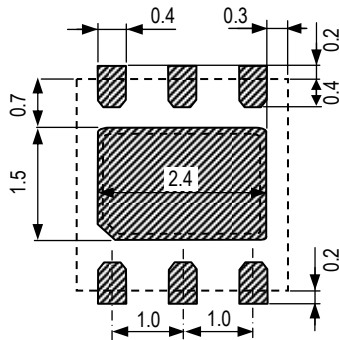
推荐 sht2x 的 PCB 设计尺寸。单位为 mm。裸焊盘（中间焊盘）与 NC 可保持悬浮或接地。外围虚线部分为 DFN 封装外部尺寸。
